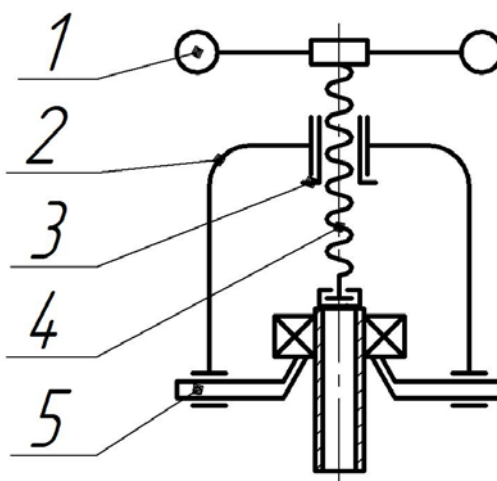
Гвинтовий знімач: 1-рукоятка; 2-корпус; 3-гайка; 4-гвинт; 5-захоплювачі.
